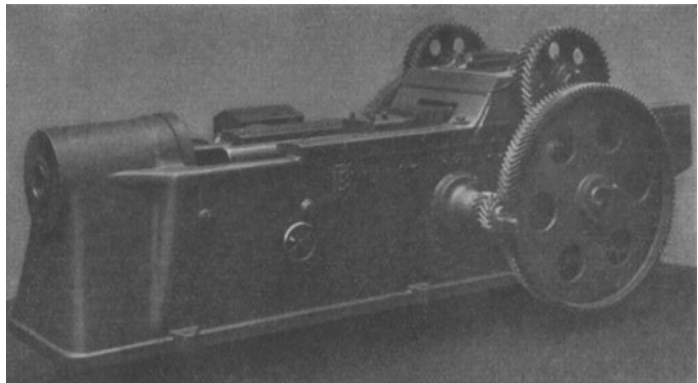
Einfachwirkende waagerechte Ziehpresse mit Stößelantrieb durch Umkehrmotor mit Zahnradvorgelege und Zahnstange. Besonders für lange Züge (Streckzüge) ohne Niederhalter.
